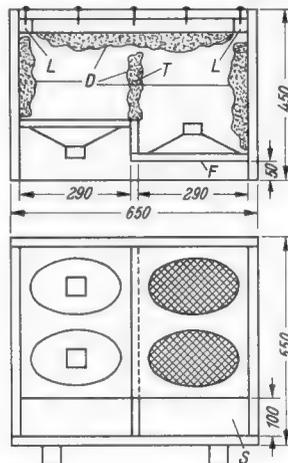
Grundriß und Frontansicht der Gegentakt-Lautsprecherbox
